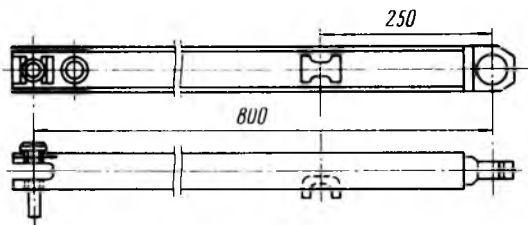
Металлический шарнирный верхняк ВВ-2
